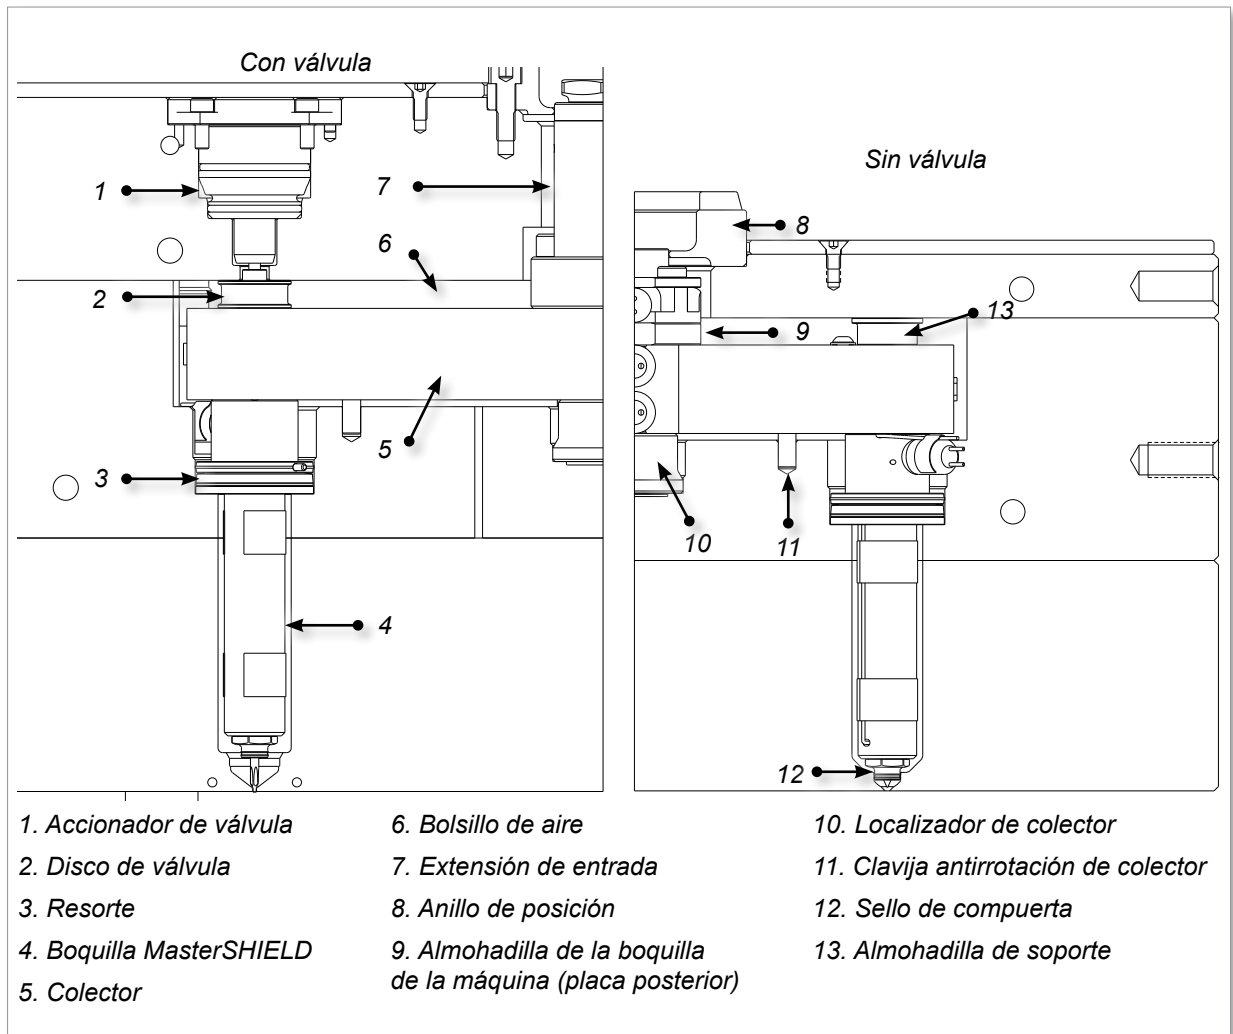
Corte de un sistema de fundición MasterSHIELD
